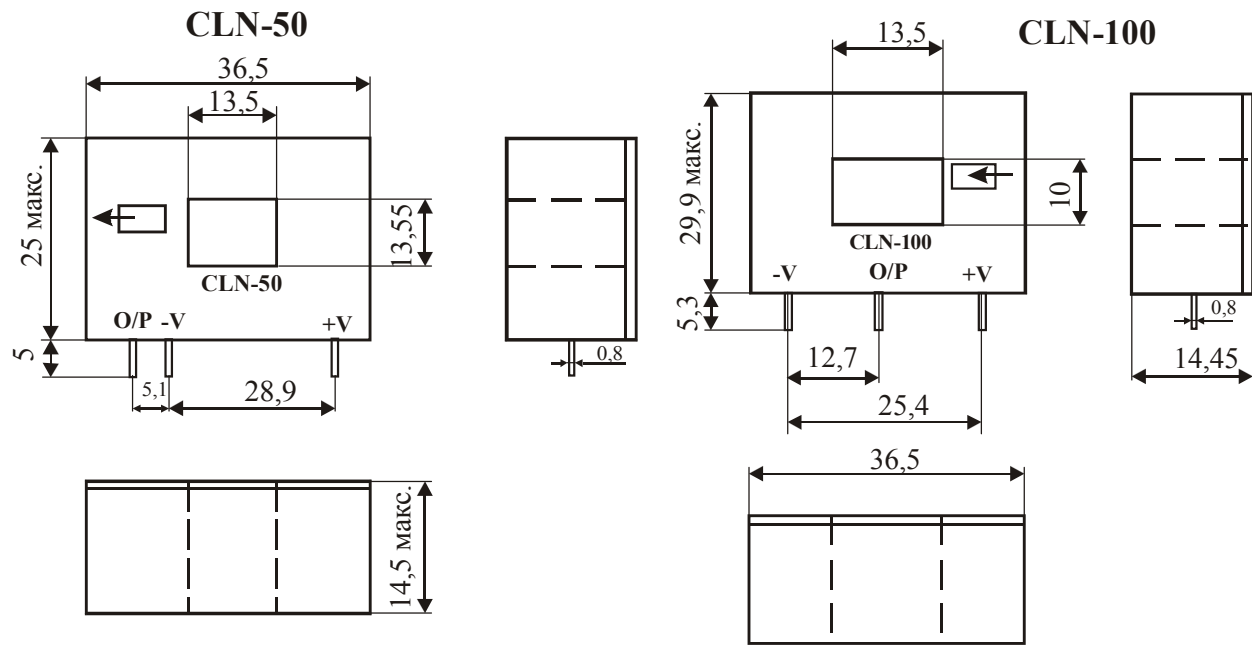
Внешний вид и габаритные размеры датчиков тока типа CLN-50, CLN-100
